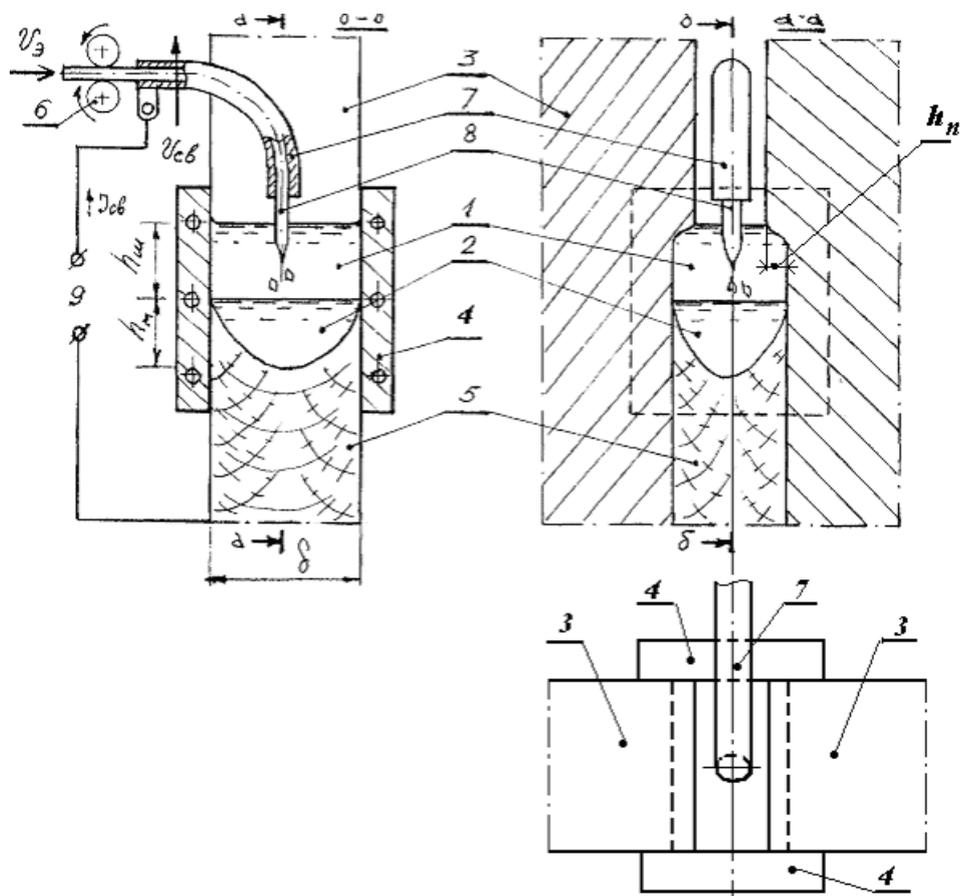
Схема процесса электрошлаковой сварки
